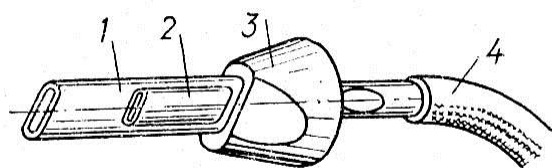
Пристрій для перевірки окремих трубок серцевини радіаторів:
